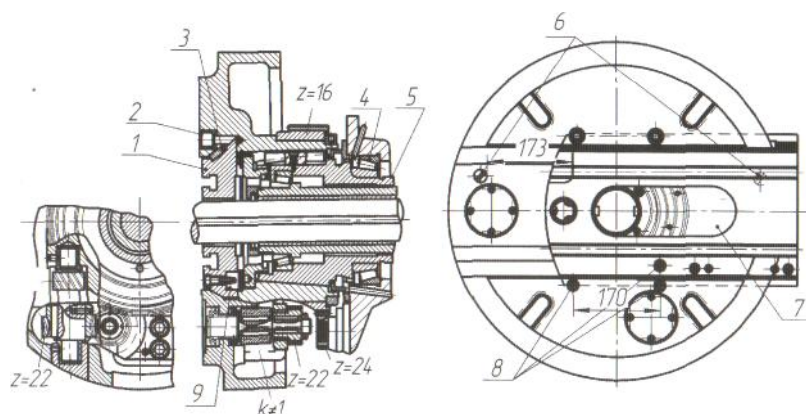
Планшайба с радиальным суппортом станка модели 262Г
